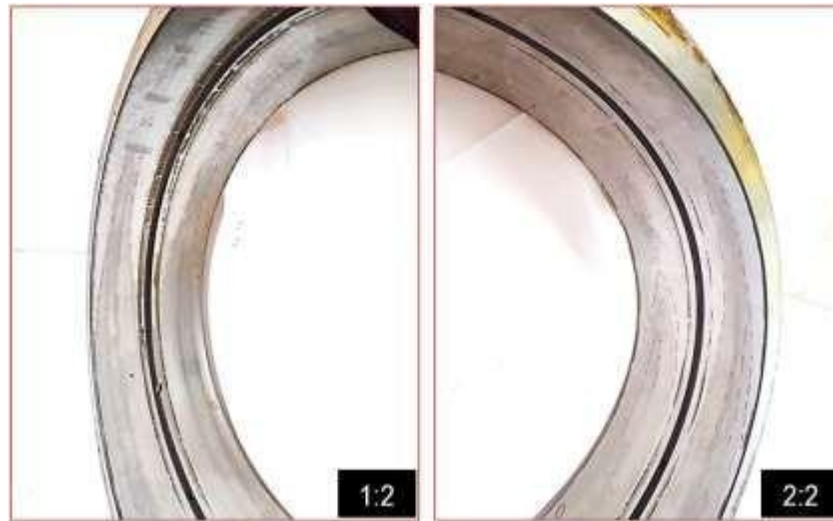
Camino de rodadura de aro exterior de rodamiento 231/560
